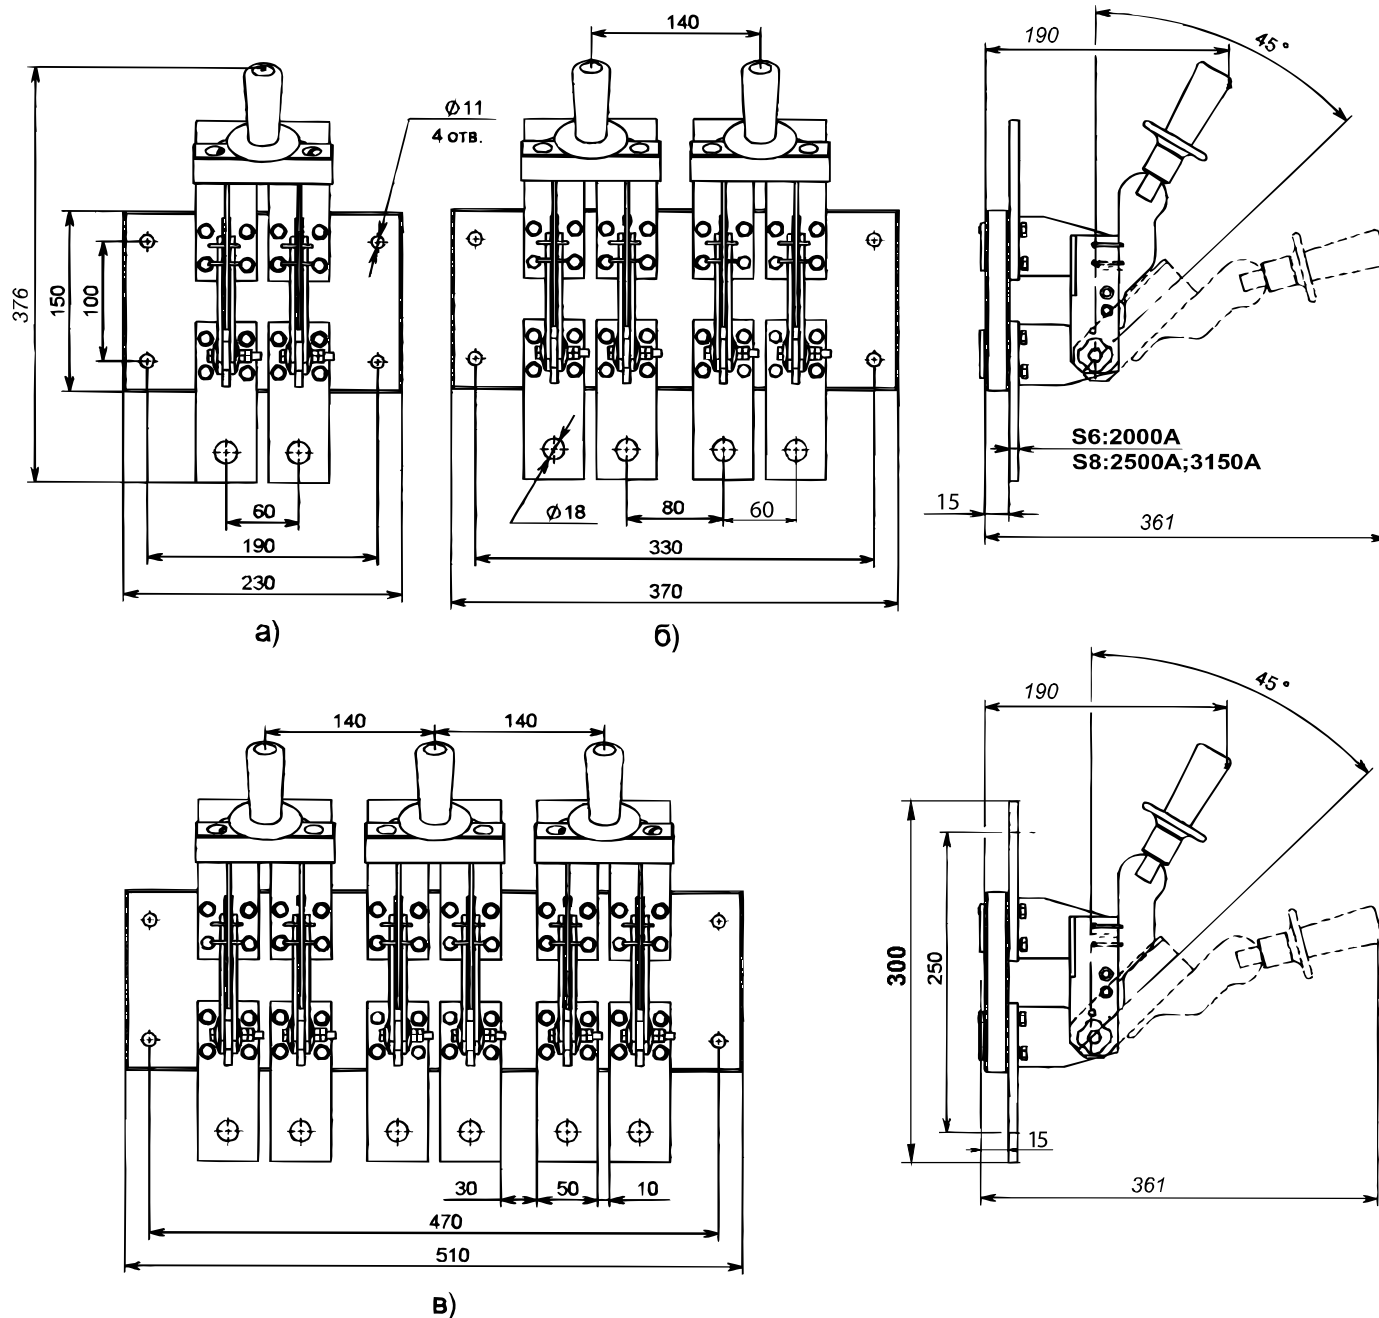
Разъединитель РЕ19 с рычагом для пополюсного оперирования штангой, на изоляционной плите
